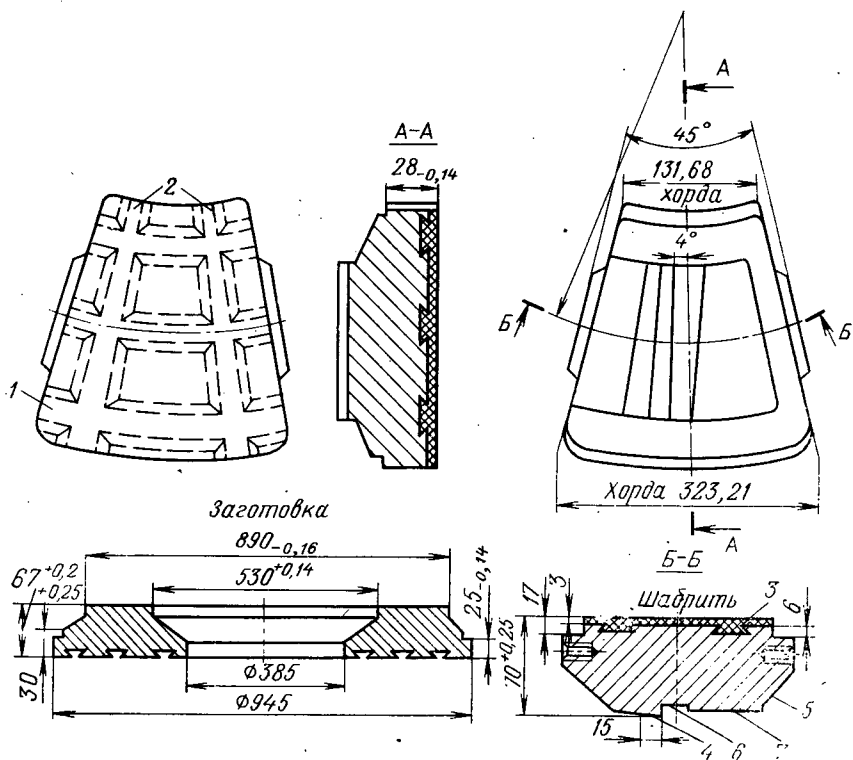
Сегмент главного упорного подшипника судовой турбины
